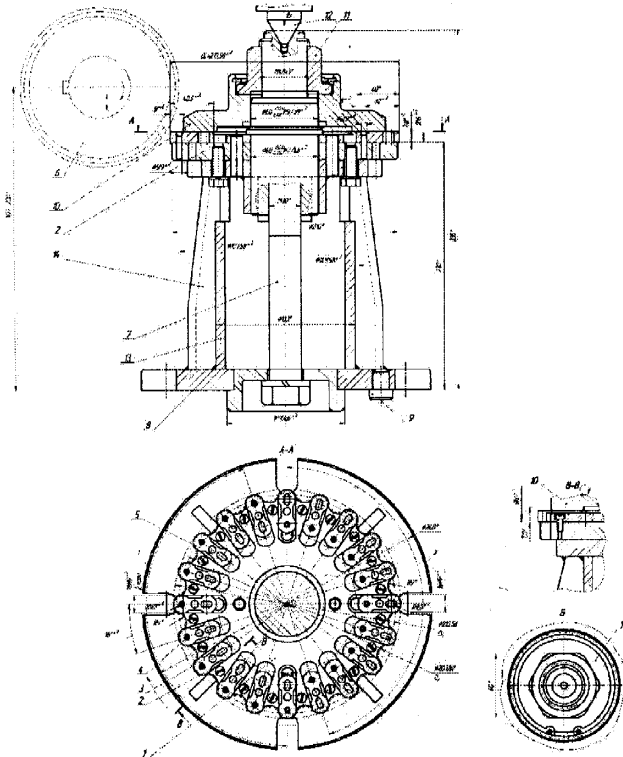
пристрій для виготовлення гальмівних елементів приводів машин на зубофрезерному верстаті
